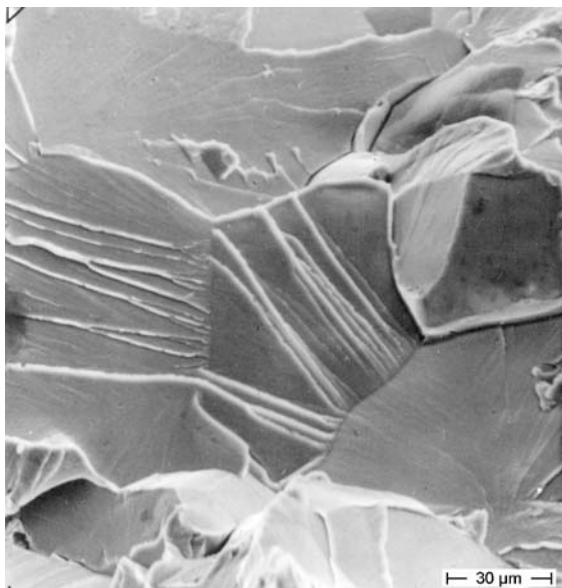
Restgewaltbruch, Spaltstrukturen mit gut ausgeprägten Flusslinien
